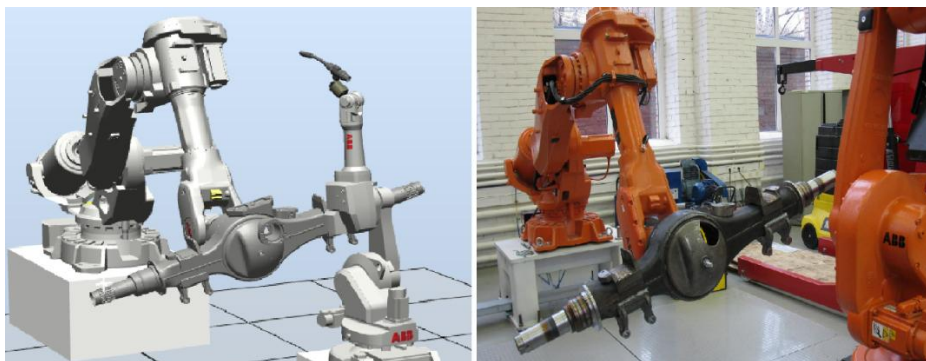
Teste virtual e real de soldadura com eixo suportado em robô
